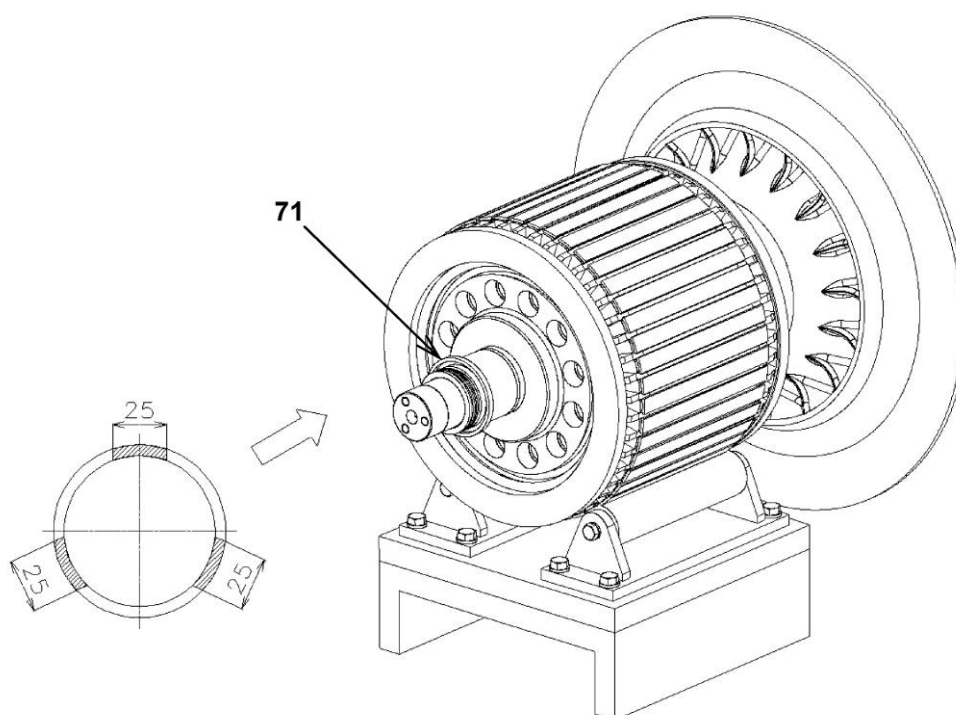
Montagem do mancal, da tampa do mancal e da junta.
